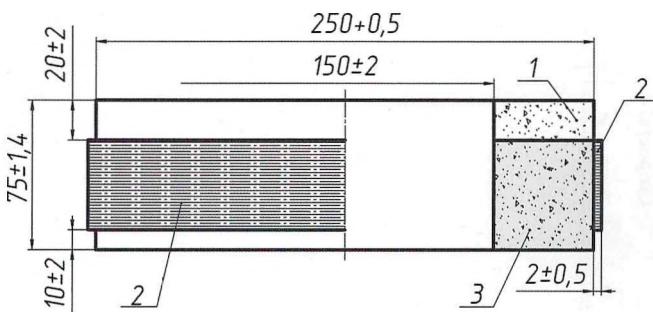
Круг абразивный для рельсошлифовальных поездов:
